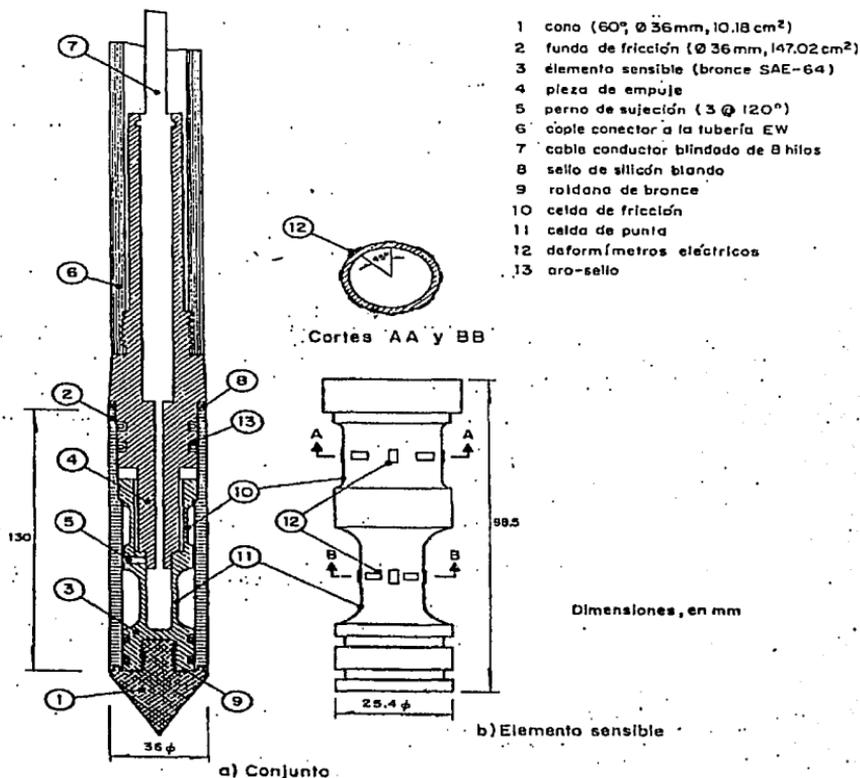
Corte transversal del penetrómetro eléctrico
